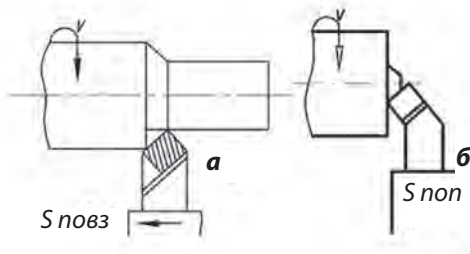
Схеми робочих рухів під час токарної обробки:
